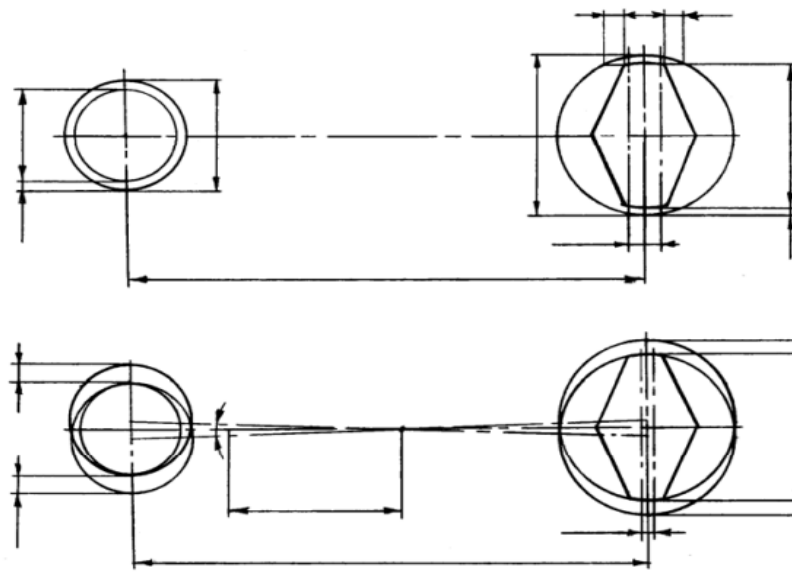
Схема установки заготовки на плоскость и два пальца:
